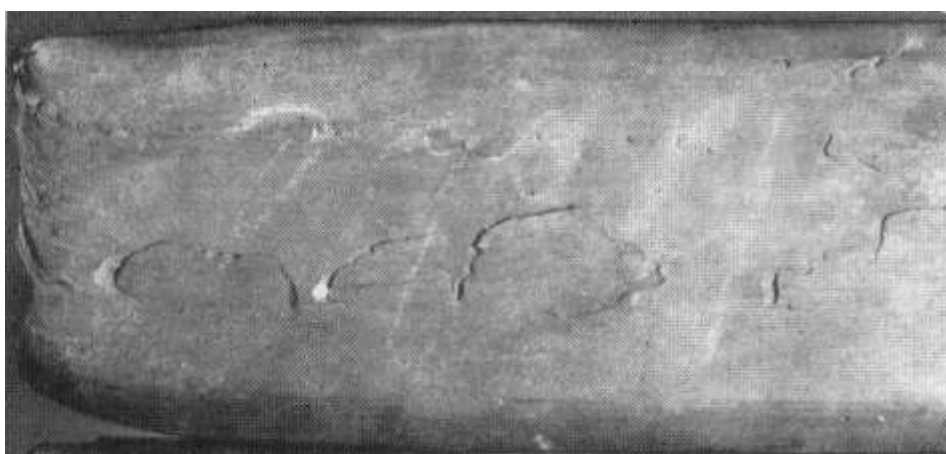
Раковины на поверхности горячекатаной заготовки
